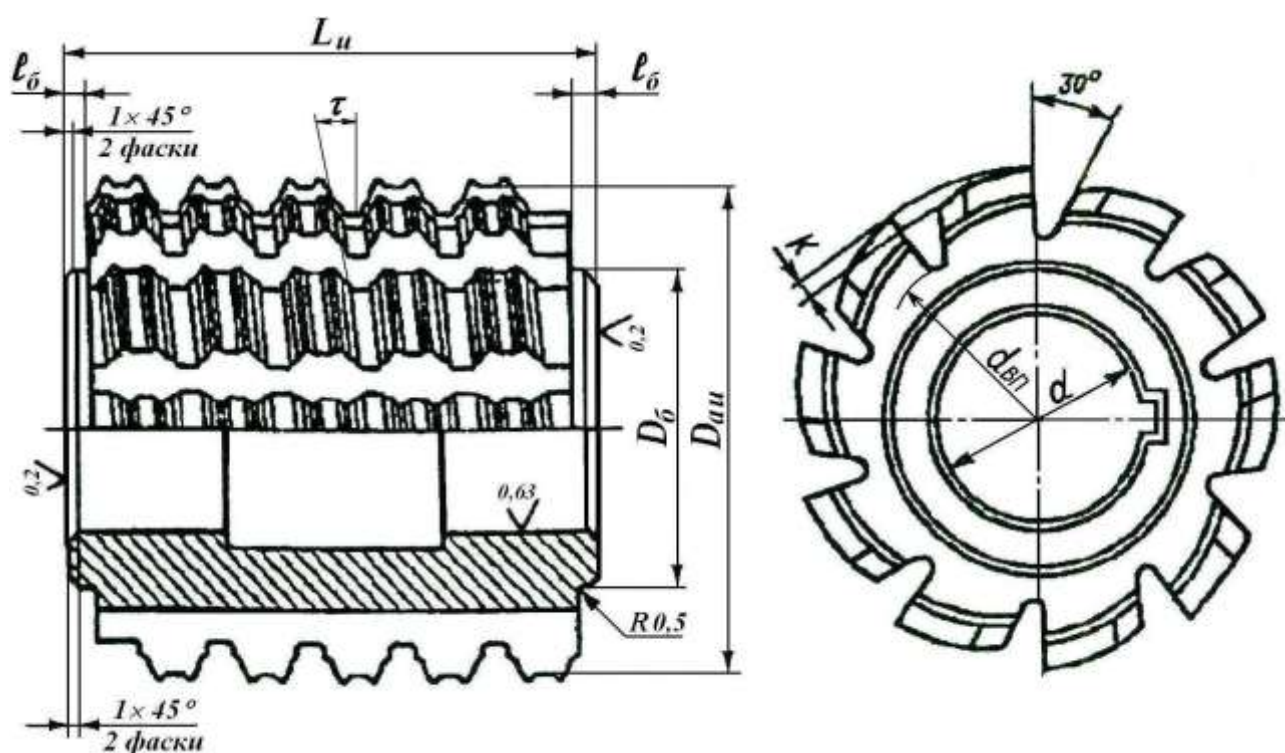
Черв'ячна фреза для обробки шліцьового вала
